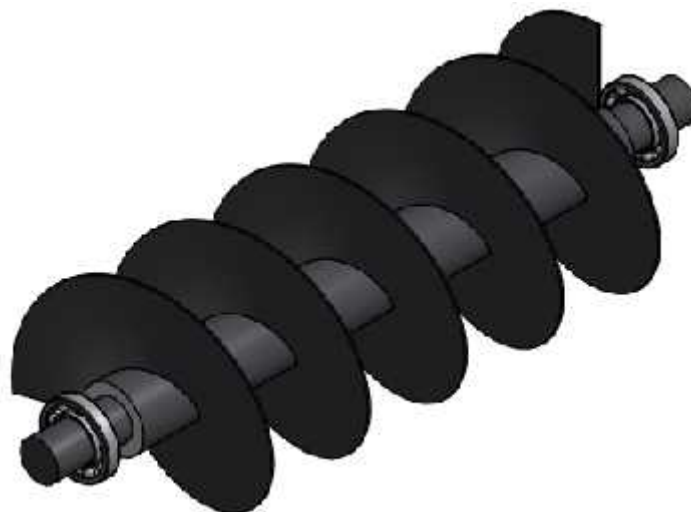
Dimensi *Screw Turbin* Dengan 5 Lempengan Blade
